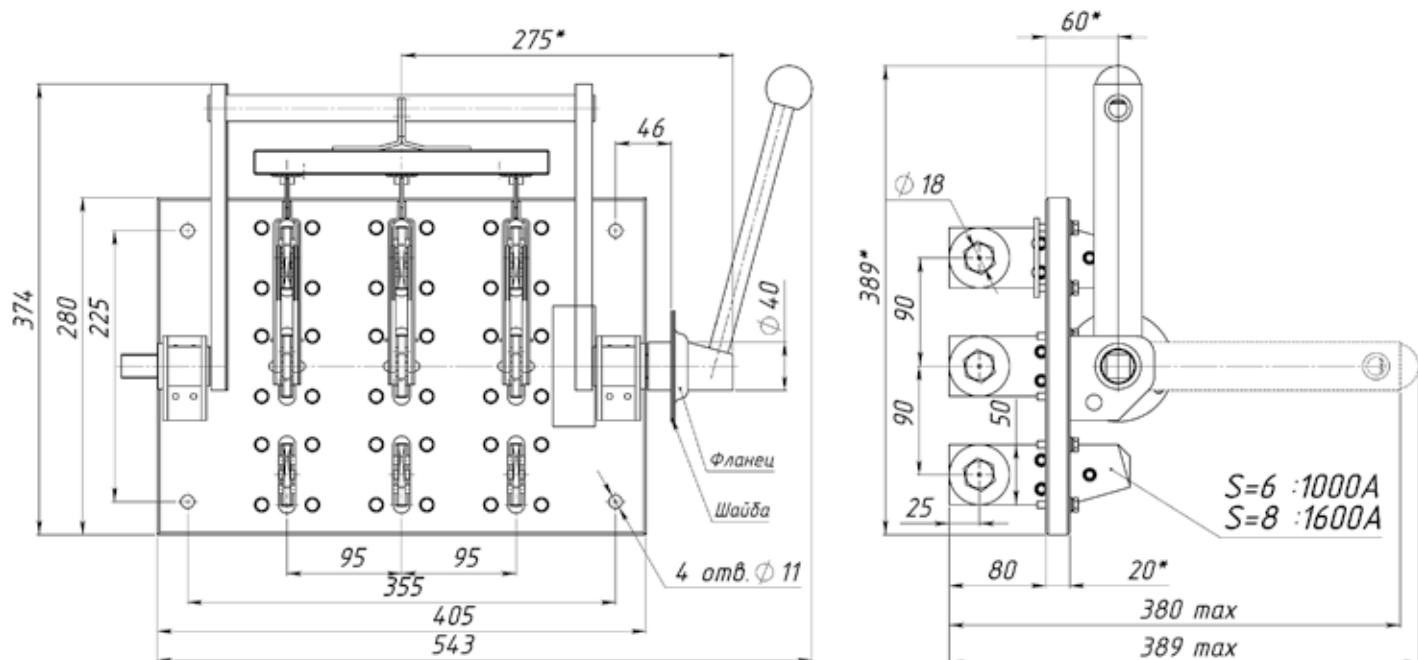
Разъединитель РЕ19-41(43)-72220-00 УХЛЗ на два направления с боковой рукояткой
